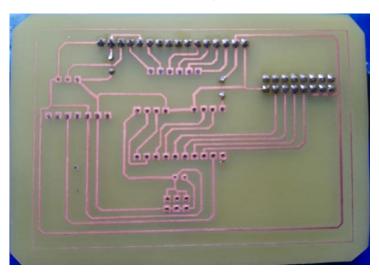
Soldadura de montaje de regletas hembras.
